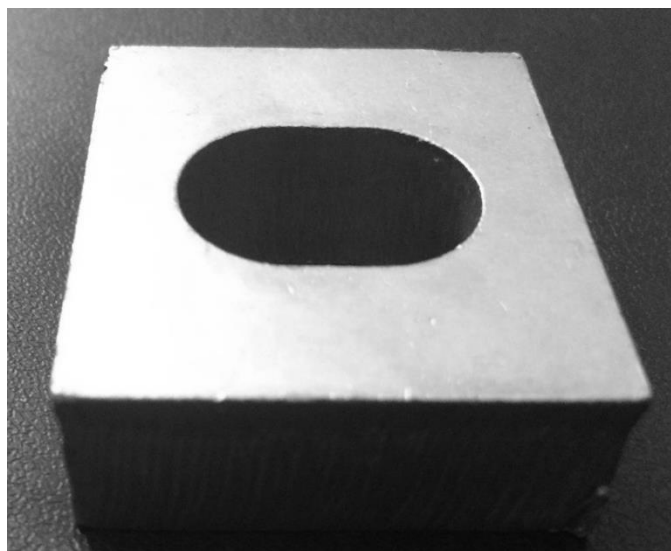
Fotografia do bloco de aço a soldar na peça estampada.
